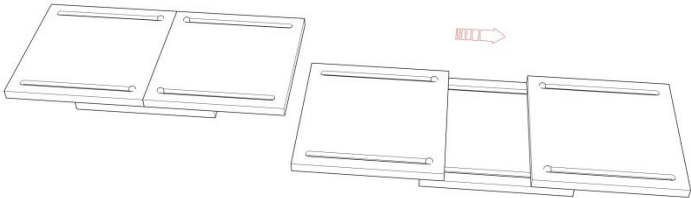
Variante concepto 2: Deslizadotes extensibles, piezas
